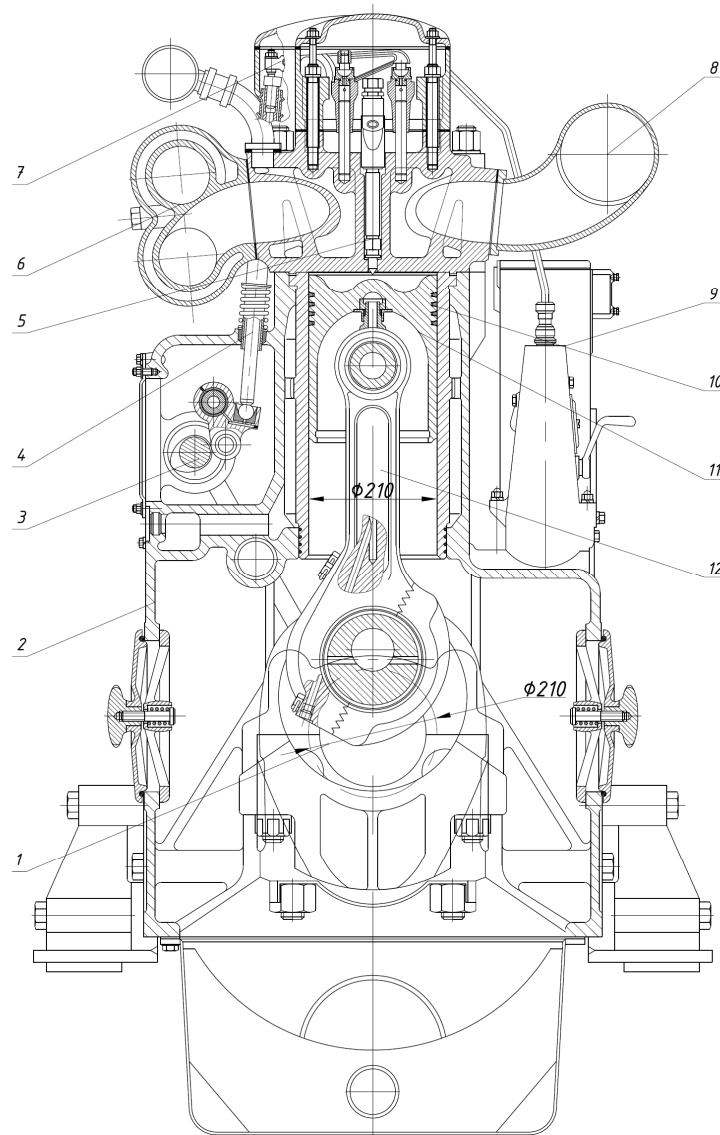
Двигун 6ЧН 21/21: 1 – колінчастий вал; 2 – картер; 3 – розподільний вал; 4 – штанга штофхача; 5 – форсунка; 6 – випускний колектор; 7 – коромисло; 8 – впускний колектор; 9 – ПНВТ; 10 – поршневі кільця; 11 – поршень; 12 – шатун
